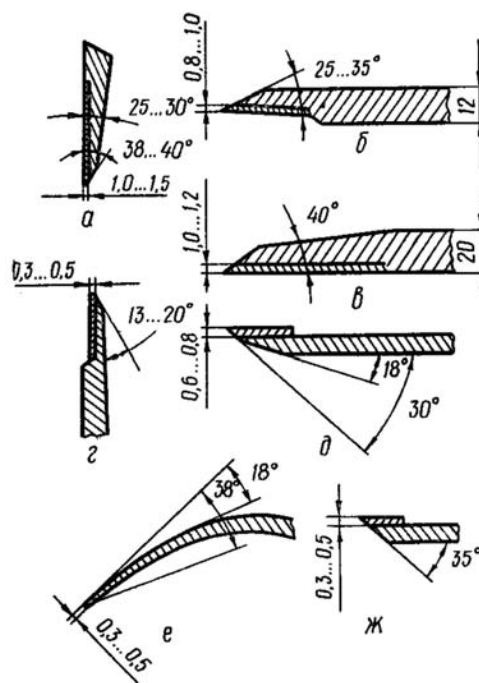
Геометрия заточки лезвий: а — лемеха плуга; б — лемеха плоскореза; в — долота плоскореза; г — лап культиватора; д — диска тяжелой бороны; е — диска лулцильника; ж — фрезы почвообрабатывающей
